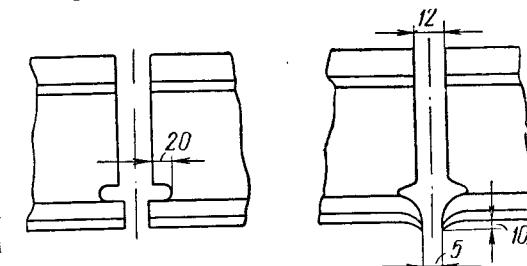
Заготовка стыка рельсов под сварку
